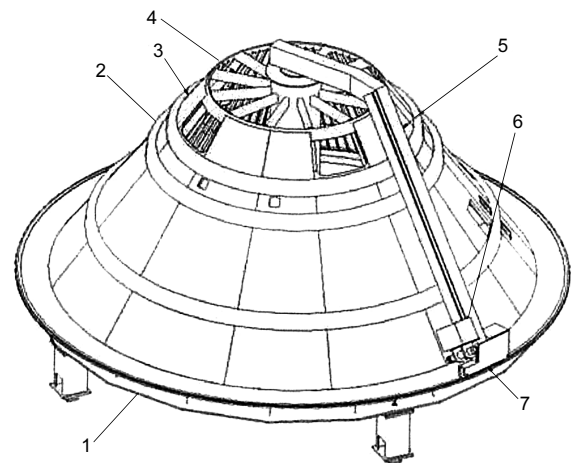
Схема кондуктора для сборки под СТП носовой части корпуса двигателя Ariane 5: 1 — нижняя опора; 2 — кольцевые рамы; 3 — соединяемые панели; 4 — верхняя опора; 5 — опорная балка для СТП; 6, 7 — тележки для осевого и радиального перемещения при СТП
